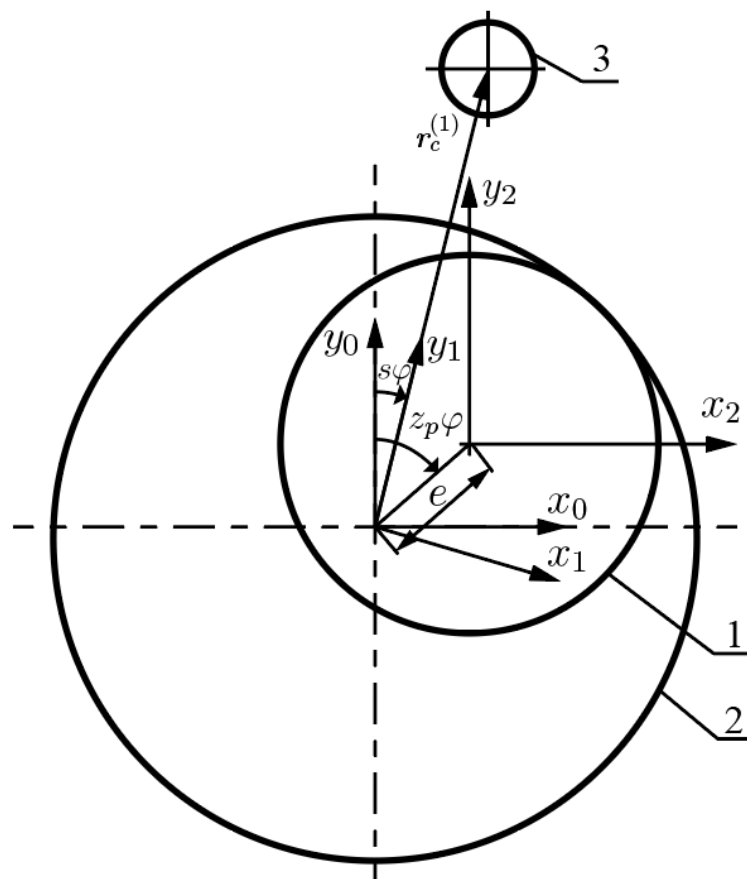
Схема планетарно-цевочной передачи: 1 – сателлит; 2 – обойма
